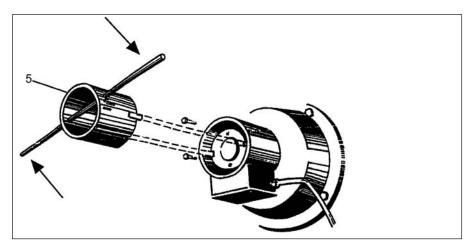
Отпуск аварийного тормоза (захватывающего устройства).
